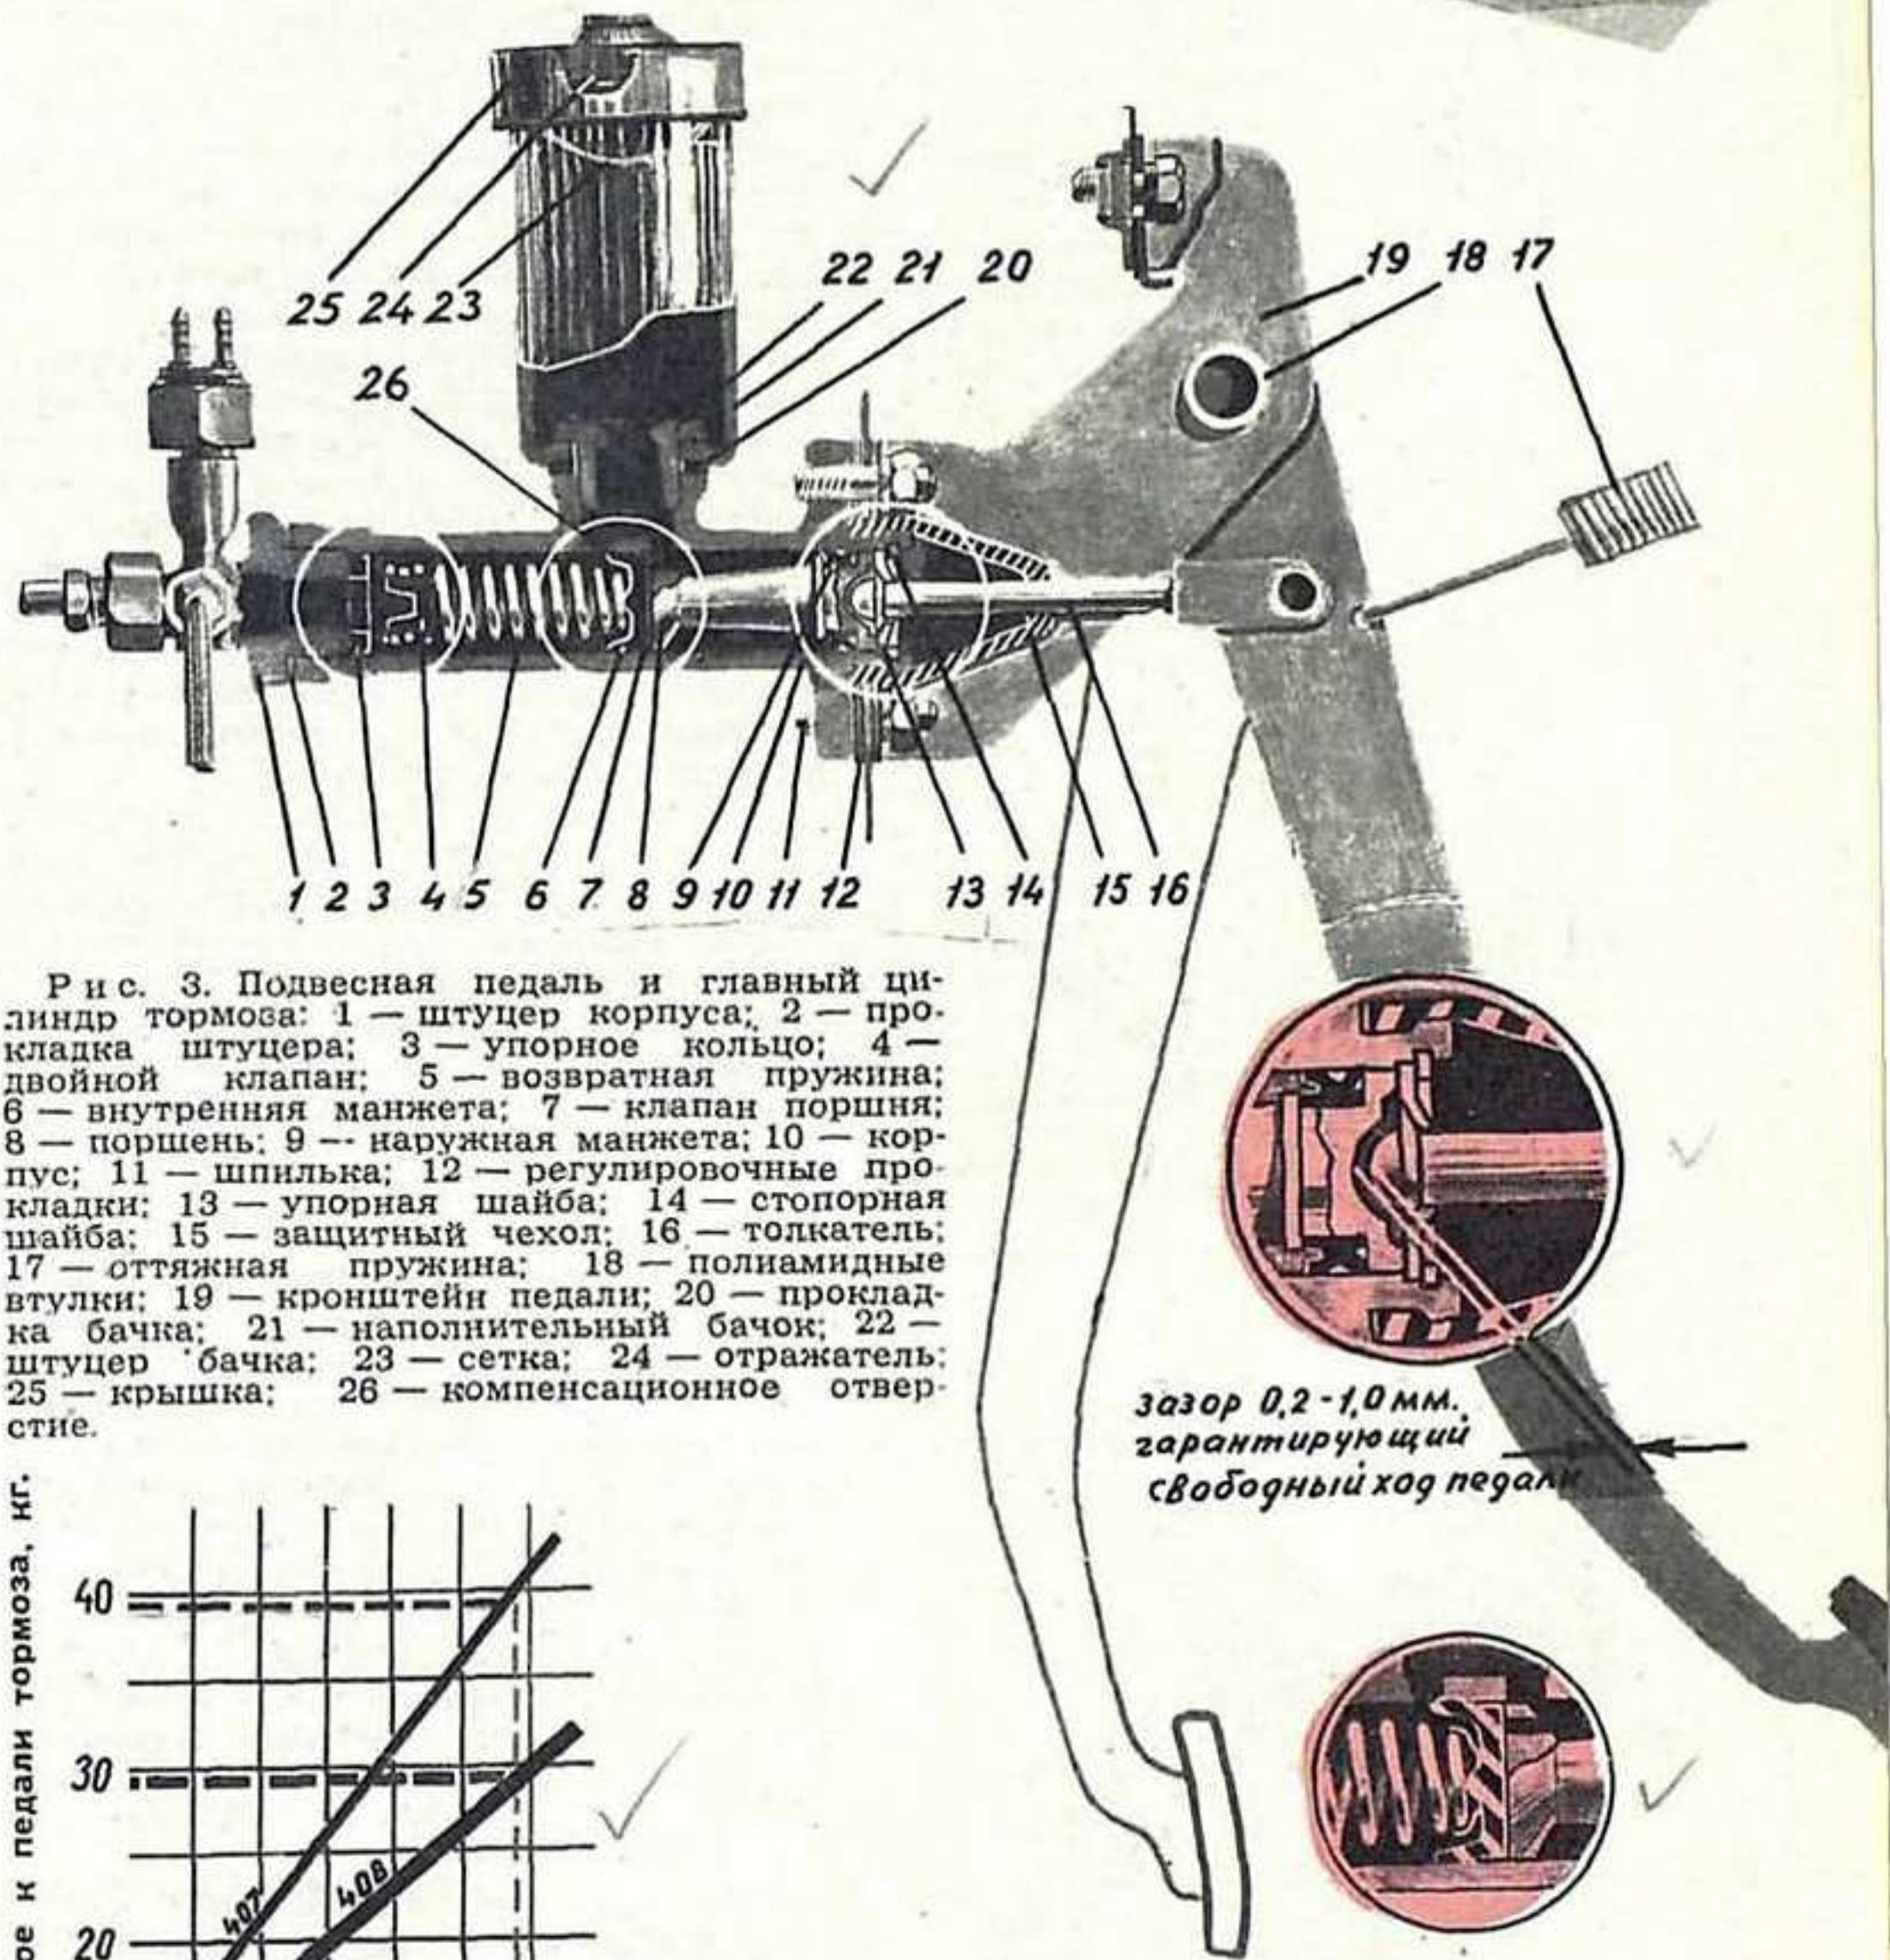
Подвесная педаль и главный цилиндр тормоза: 1 — штуцер корпуса; 2 — прокладка штуцера; 3 — упорное кольцо; 4 — двойной клапан; 5 — возвратная пружина; 6 — внутренняя манжета; 7 — клапан поршня; 8 — поршень; 9 — наружная манжета; 10 — корпус; 11 — шпилька; 12 — регулировочные прокладки; 13 — упорная шайба; 14 — стопорная шайба; 15 — защитный чехол; 16 — толкатель; 17 — оттяжная пружина; 18 — полиамидные втулки; 19 — кронштейн педали; 20 — прокладка бачка; 21 — дополнительный бачок; 22 — штуцер бачка; 23 — сетка; 24 — отражатель; 25 — крышка; 26 — компенсационное отверстие.
